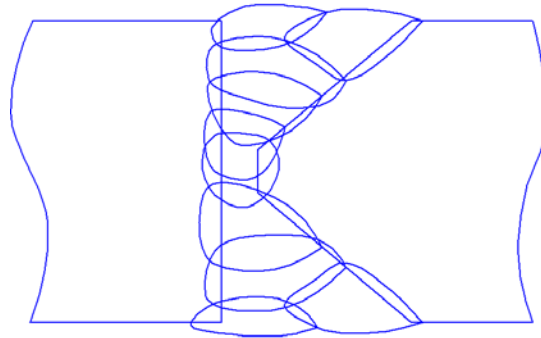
Схема раскладки валиков по сечению металла шва К-образного сварного соединения сталей 04Х20Н6Г11М2АФБ, выполненного присадочной проволокой ЭП-263Ш
